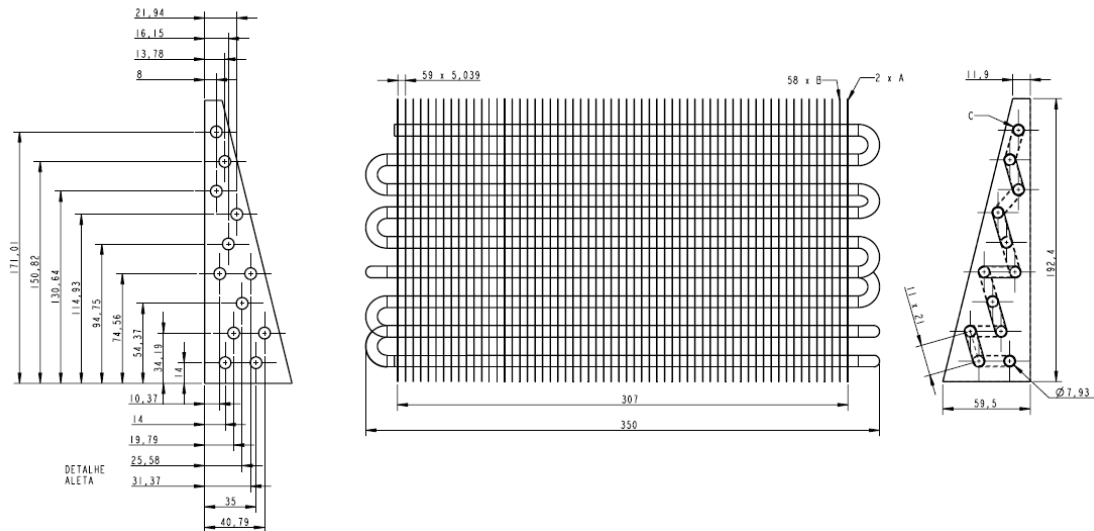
Desenho técnico e cotas para os EFA 1/5 1, 30 e 60 aletas.
